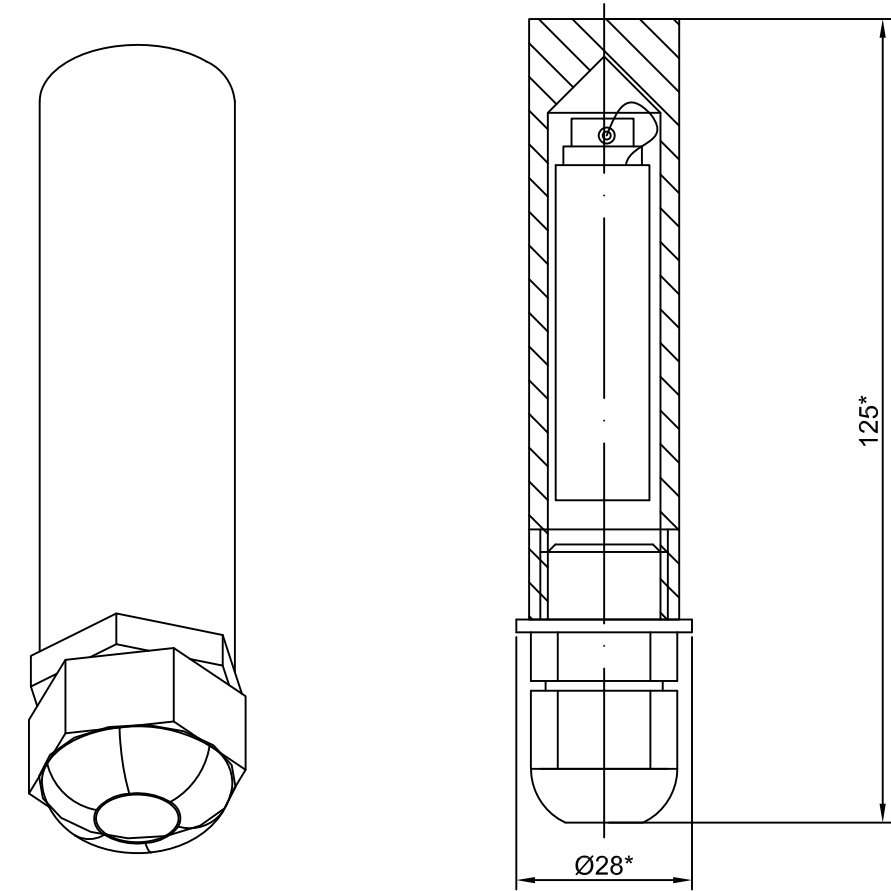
РЧС-Т. Общий вид и габаритные размеры
